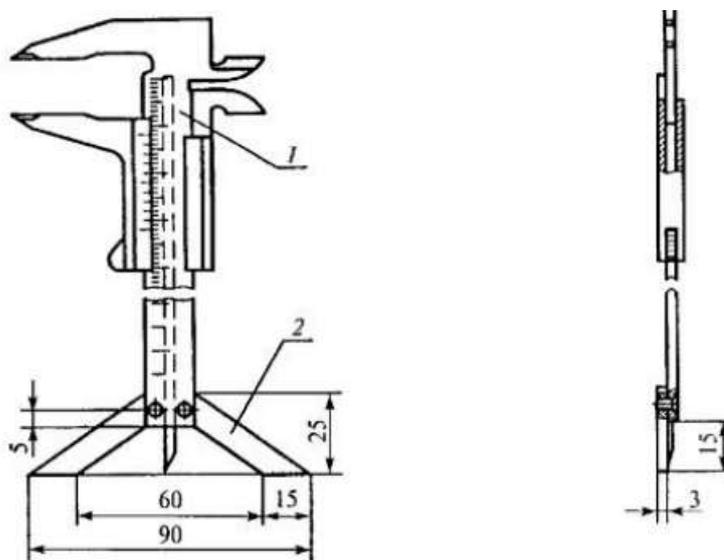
Штангенциркуль типа ШЦ- 1 с опорой
